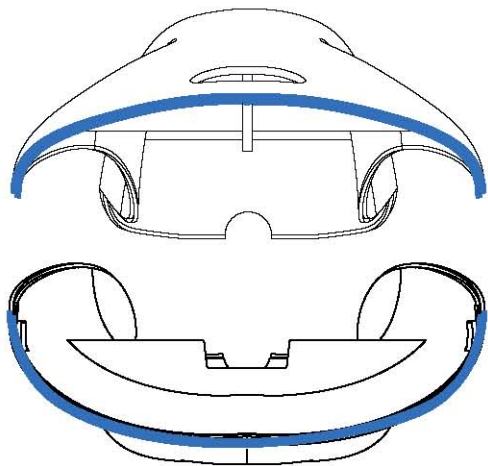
Ensamble de carcasas por acoplamiento y soldado por ultrasonido.
